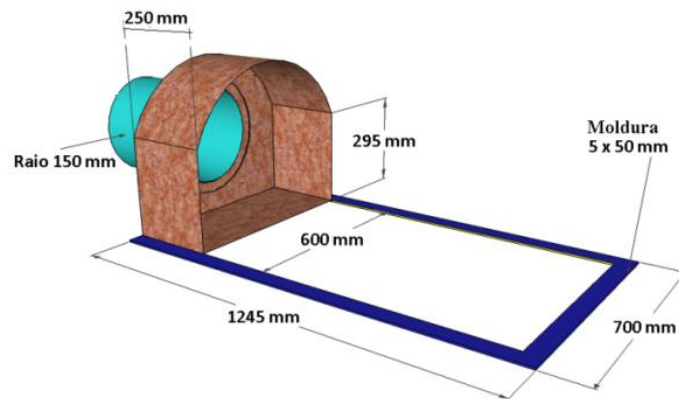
Caixa coletora com abertura para saída do ar, montada sobre a moldura do trocador.
